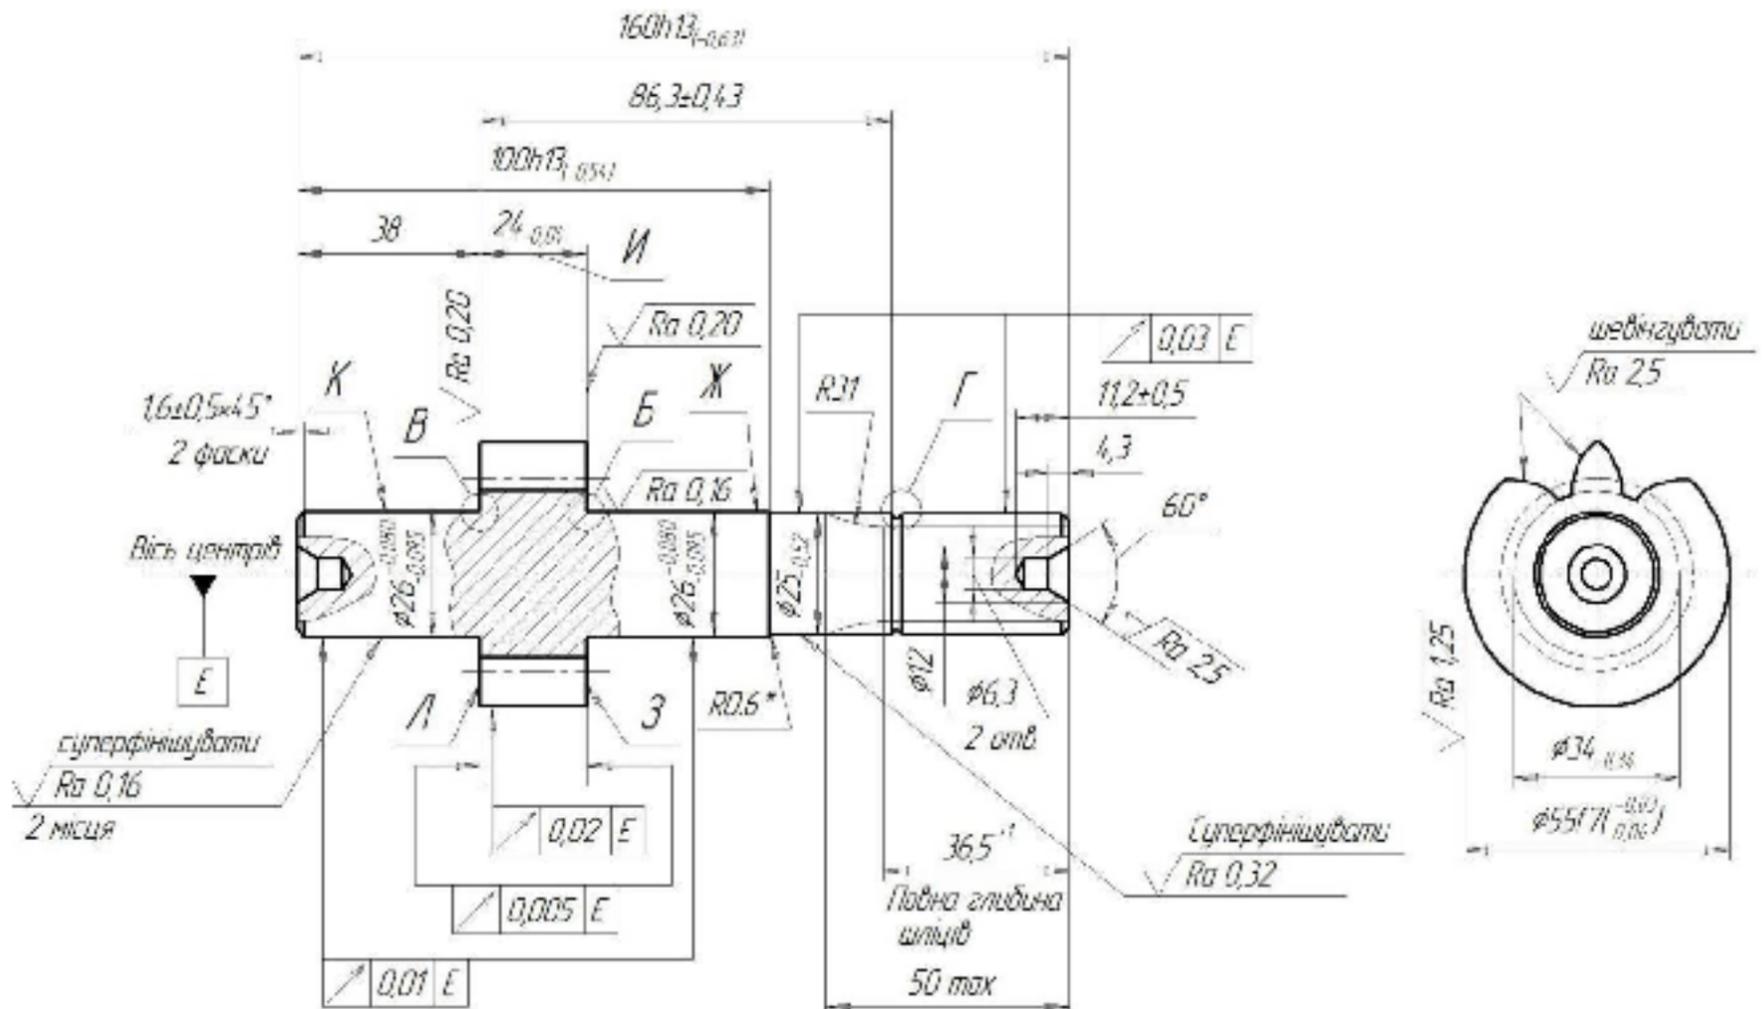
Ескіз деталі «Вал-шестерня 32-3.005»
